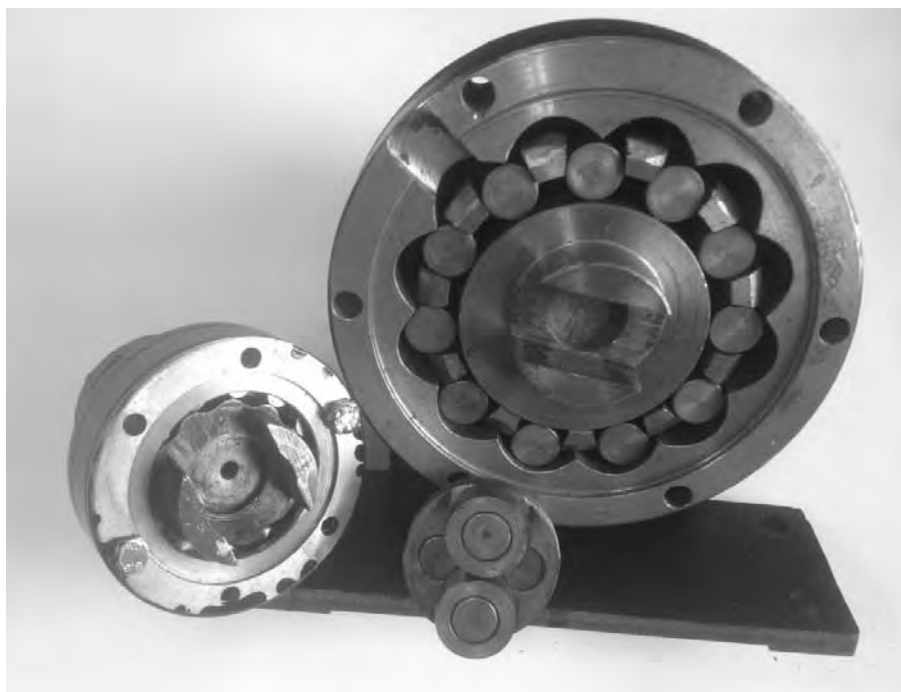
Общий вид опытного образца двухступенчатого редуктора с промежуточными телами качения радиального типа во второй ступени
